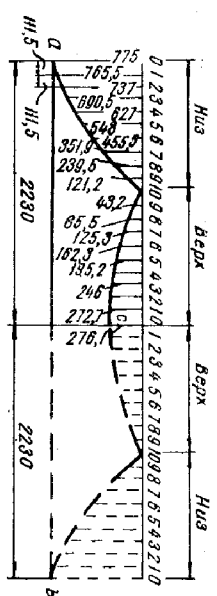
Разметка конца трубы II разветвленного сварного тройника (штатен).
